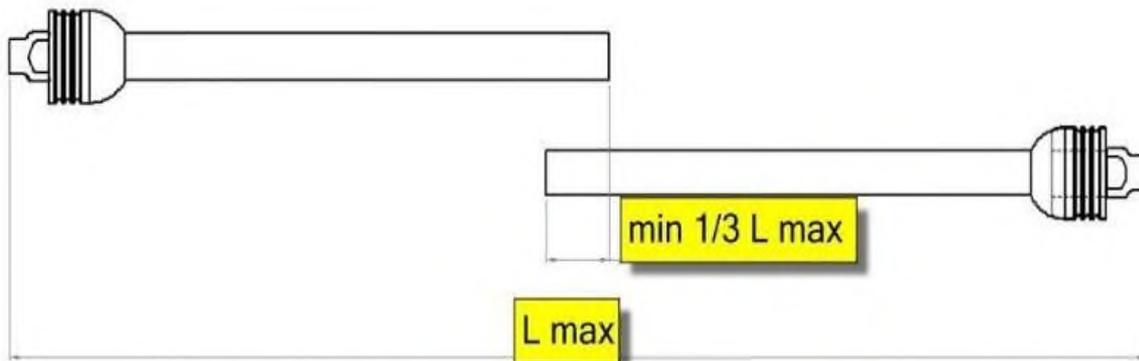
Longitud de las cubiertas del árbol articulado-telescópico
